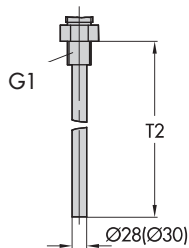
· Dimensions, vanne type 2114 équilibrée par membrane avec raccord pour thermostat type 2231 à 2235
